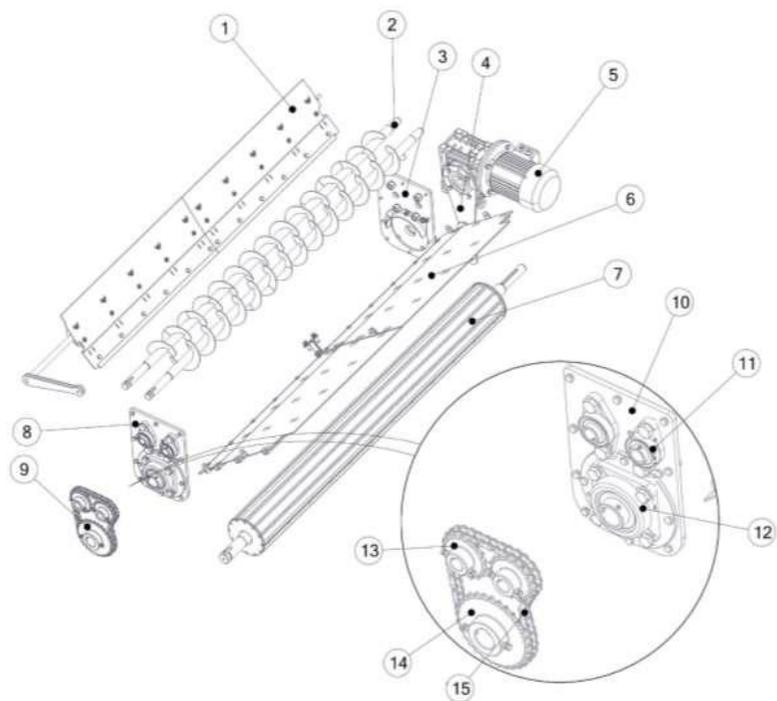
Шнеково - валковый распределительный механизм. Общий вид в сборе.
